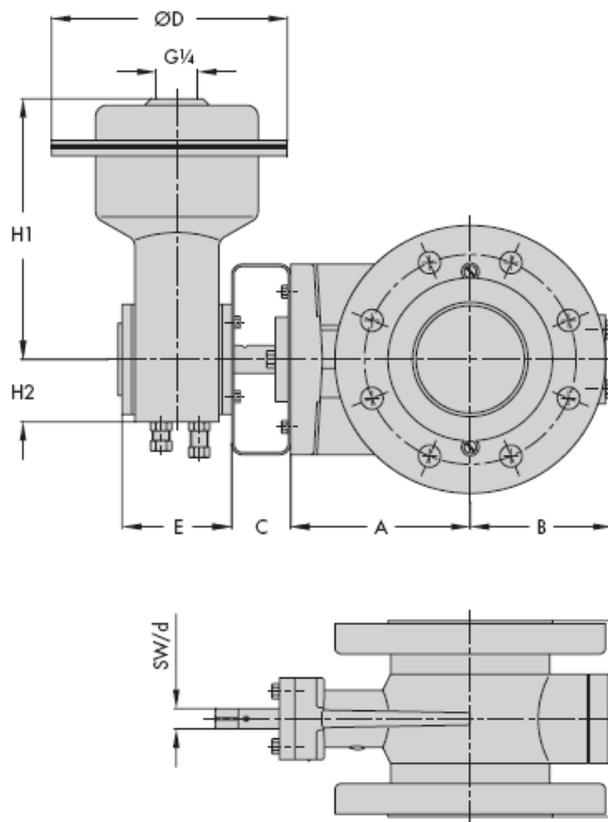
• Габаритные размеры Тип 3310 / 3278
